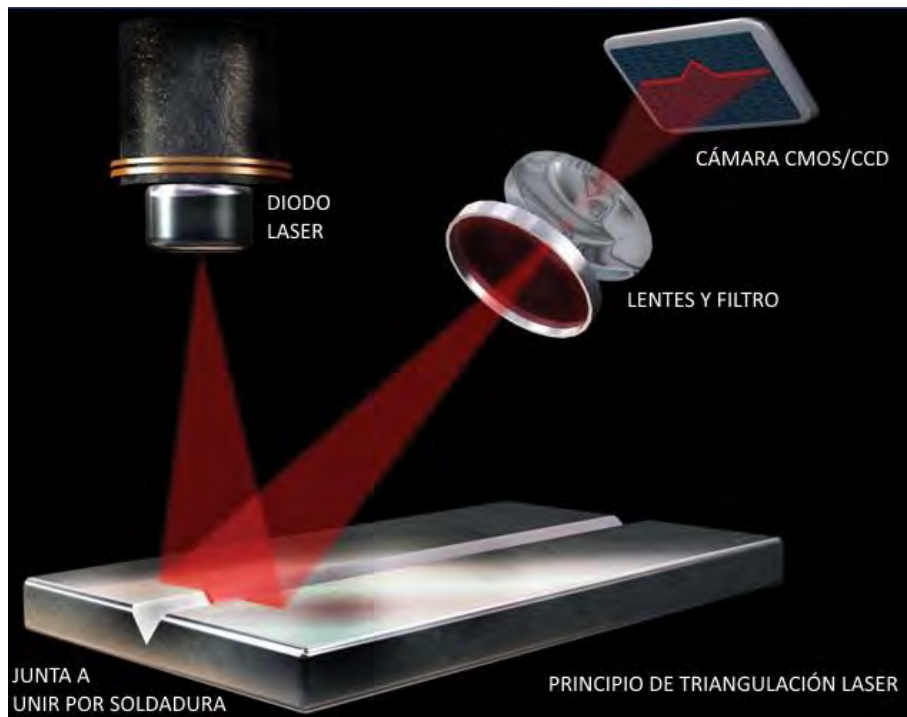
Principio de visión láser, Fuente: The tube & pipe journal, setiembre 2014
